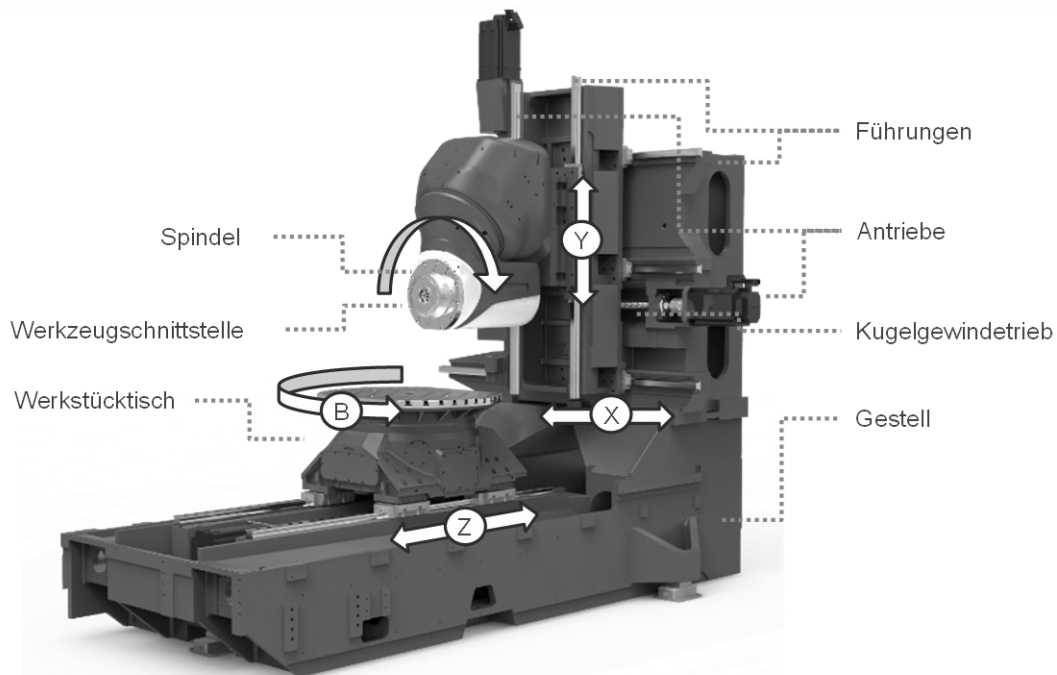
Komponenten und Achsen der Werkzeugmaschine [HIR16] (Quelle Maschine: DMG)
